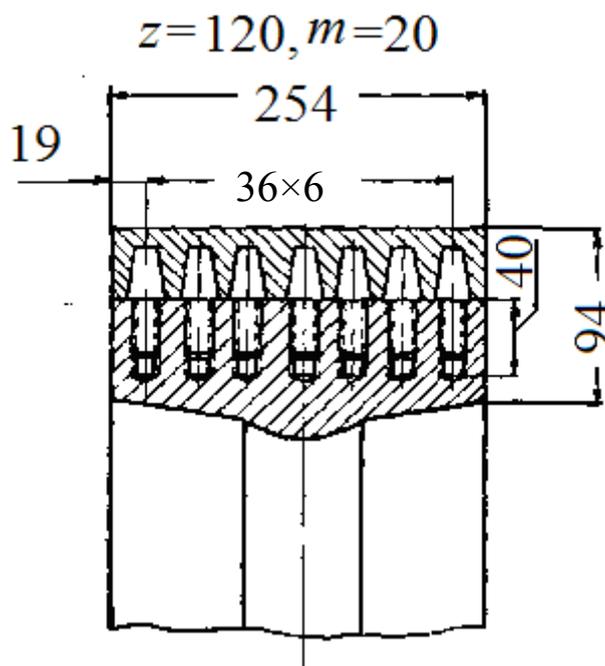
Замена разрушенного зуба при помощи шпилек и их обварки
